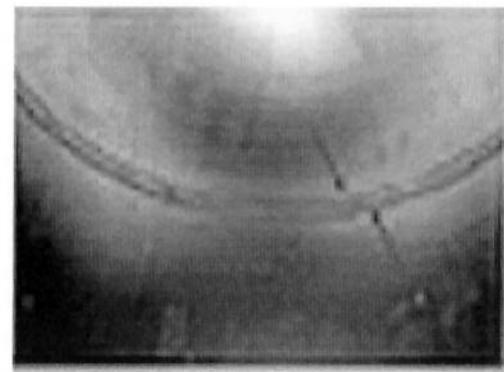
Região soldada apresentando corrosão⁷
